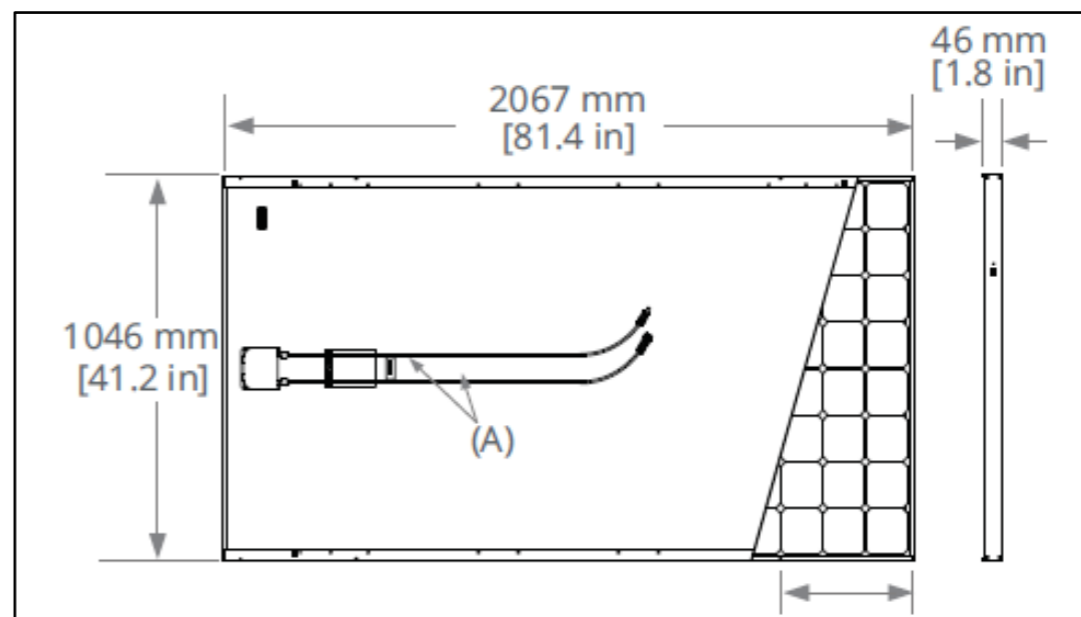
Schéma d'un panneau (source : Sun Power 440 Wc)
